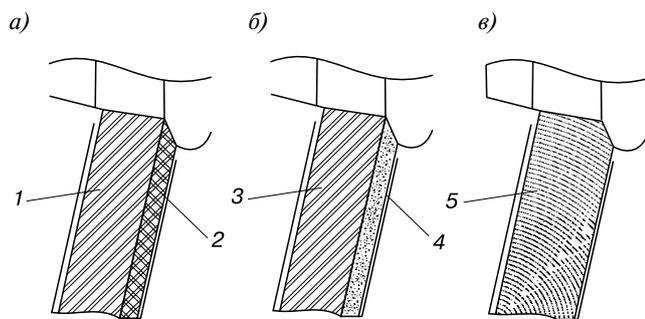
Схема комбинированного металлополимерного плакирования поверхности гребня и тяговой поверхности круга катания колеса: а – комбинированное металлополимерное плакирование; б – комбинированное металлоплакирование; в – реализация анизотропных фрикционных связей;
